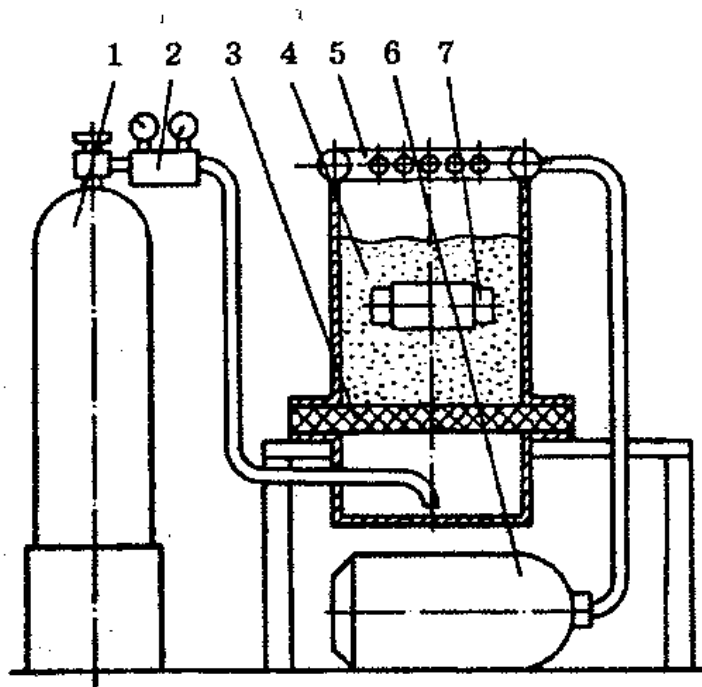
Схема пристрою для нанесення полімерного покриття в псевдозрідженому шарі: 1- балон зі стисненим повітрям або азотом; 2 - редуктор; 3 - пориста перегородка; 4 - камера; 5 - витяжний пристрій; 6 - пилосмок; 7 - заготовка
